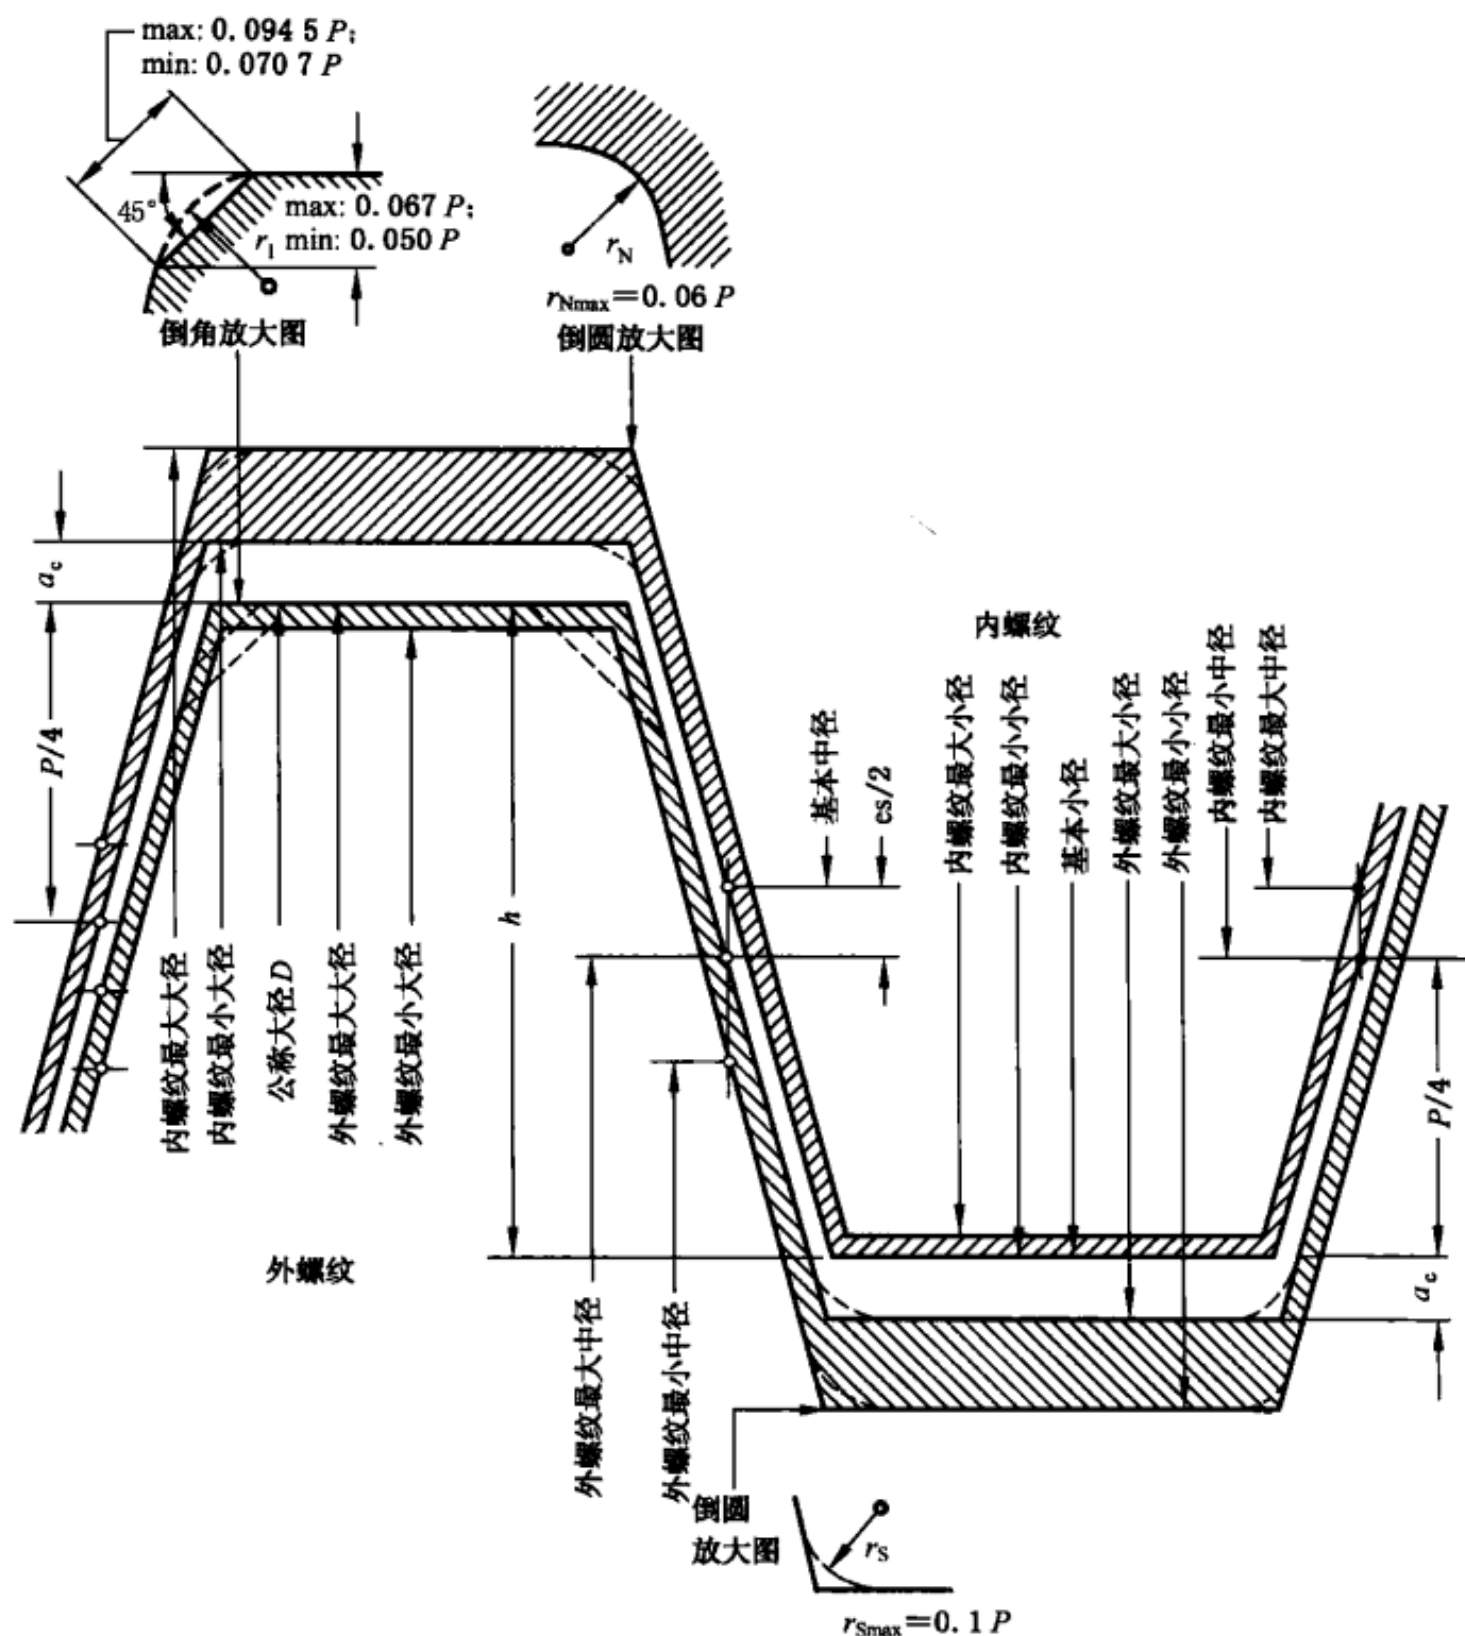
一般用途爱克母螺纹的公差带位置
